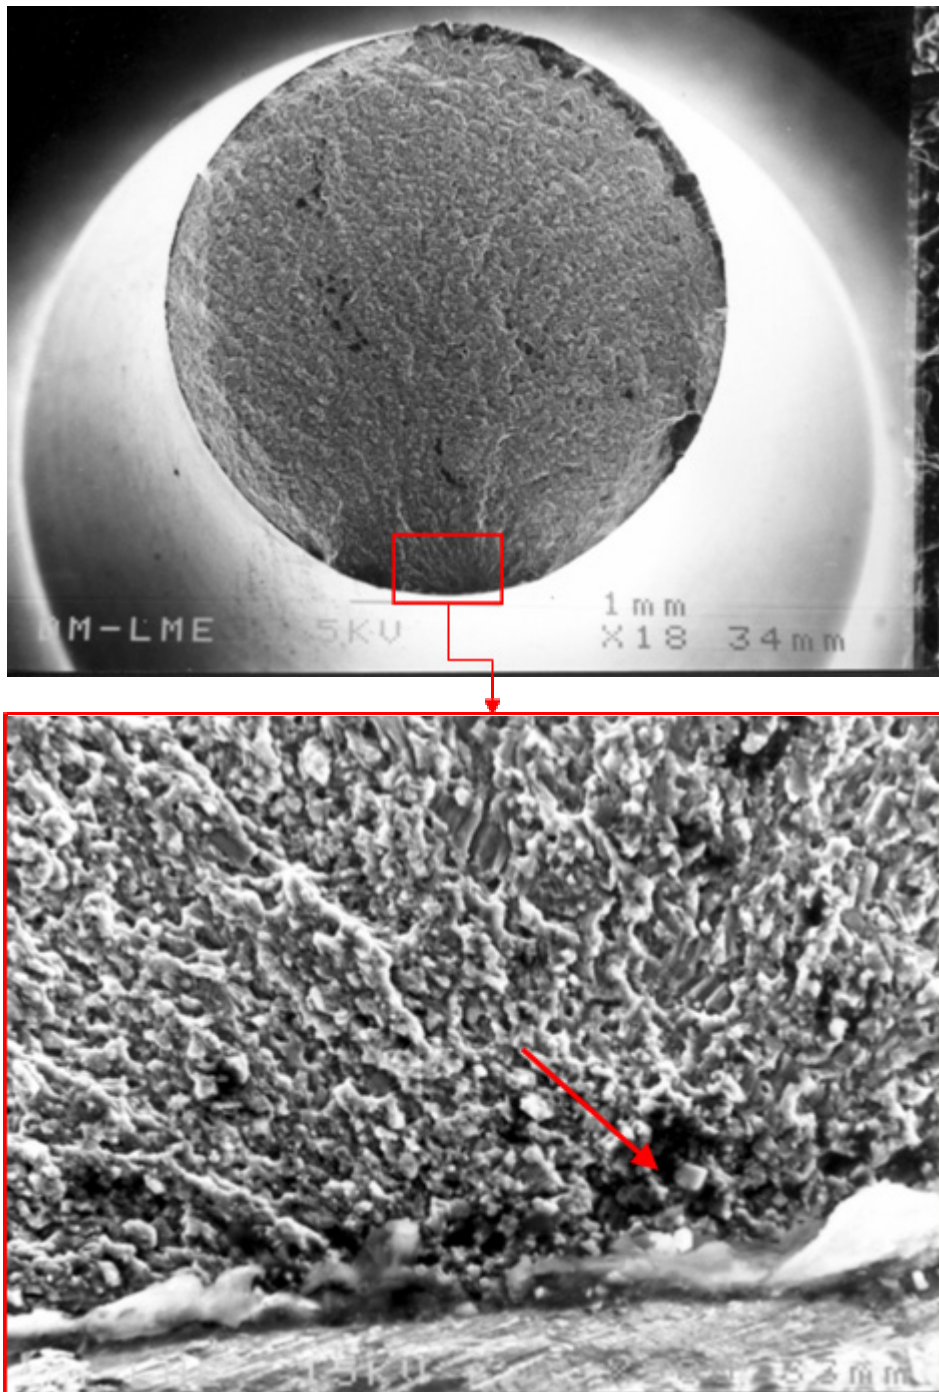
Aglomerado de partículas de SiC en el origen de la grieta de fatiga en una probeta del material A2124/SiC/17p T4, fracturada a 83000 ciclos, solicitada a una tensión máxima de 490 MPa y para una R de 0,6: a) aspecto general, b) detalle de la zona de inicio de la fractura.
